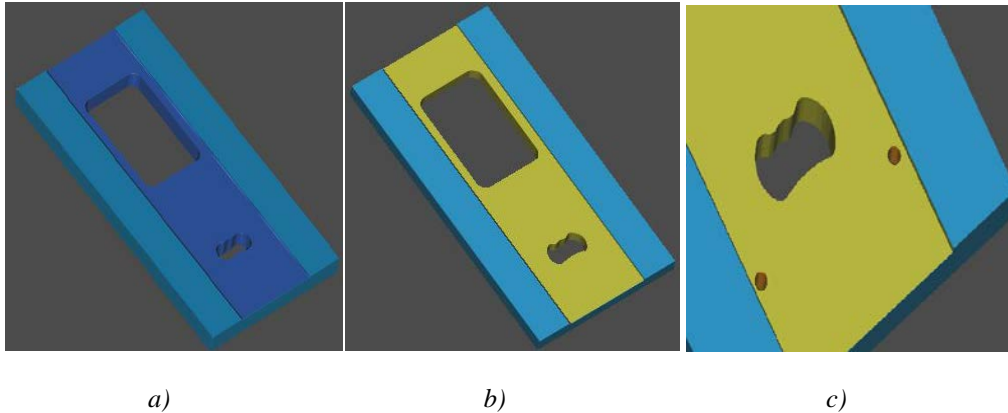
a) Placa guía de punzones maquinada con cortador de 12.7 [mm]. b) Placa guía de punzones maquinada con cortador de 4.76 [mm] c) Placa guía de punzones maquinada con cortador de 3.175[mm].
